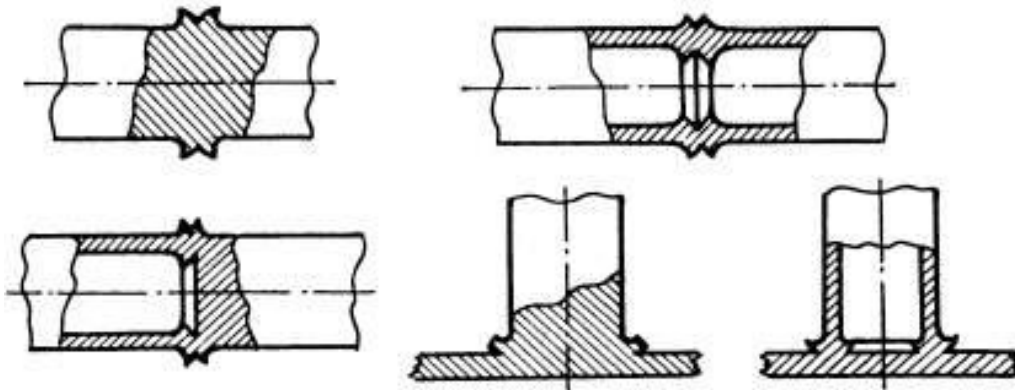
Типы сварных соединений, выполненных сваркой трением
